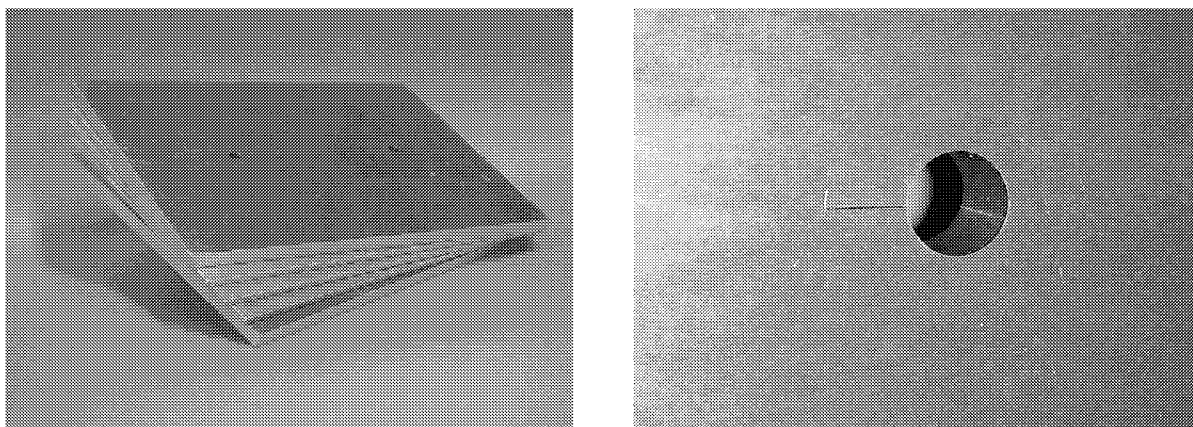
Aluminiumplatten der Dicken 5 mm und 10 mm mit zwei Nietbohrungen des Durchmessers 8 mm (links) und Aluminiumplatte der Dicke 30 mm mit drei Nietbohrungen des Durchmessers 25 mm (rechts).
